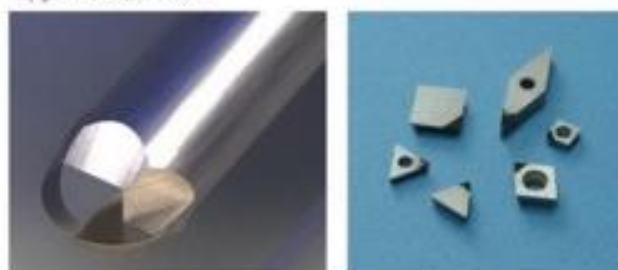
Фреза для высокоскоростного фрезерования с рабочей частью из CVD-алмаза и твердосплавные пластины с вставками из CVD-алмазов.
